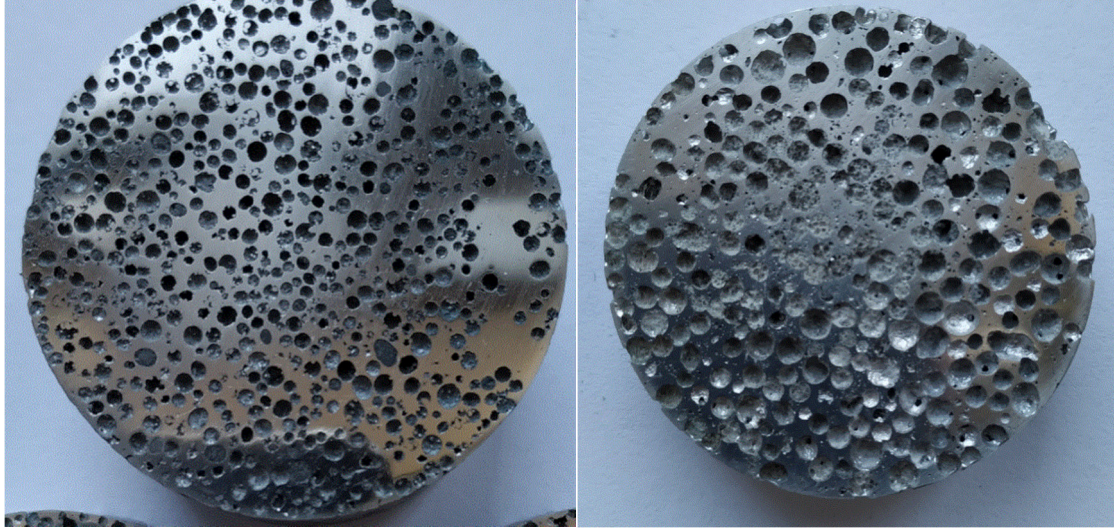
a) 1-2 ve b) 2-4 mm Çapa Sahip Genleştirilmiş Cam Küre Takviyeli Sintaktik Köpük Metaller
